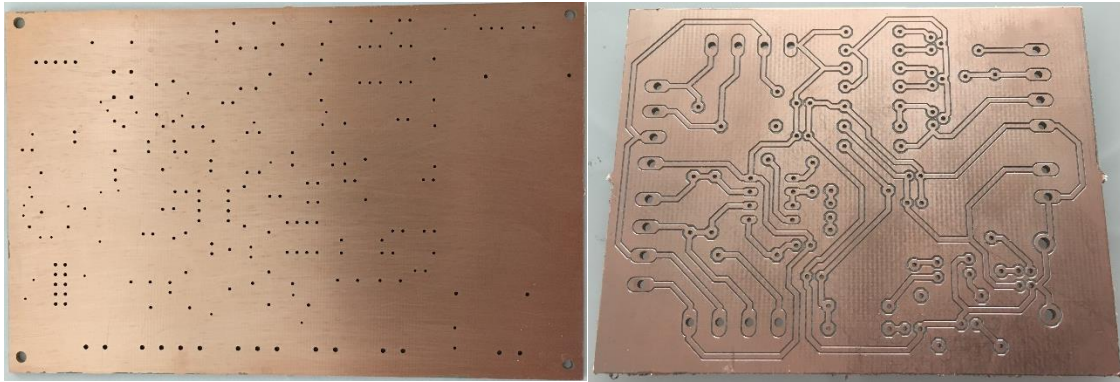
PCB perfurada (esquerda) e circuito fresado (direita)
